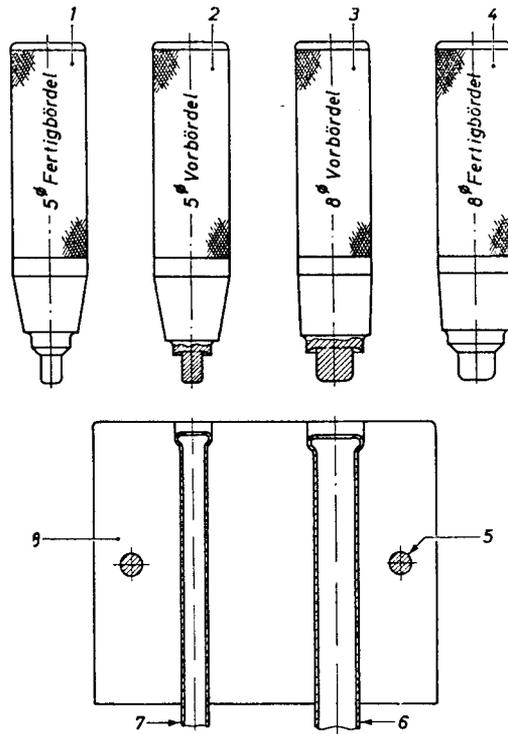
Anwendung des Bördelwerkzeuges S-1066
